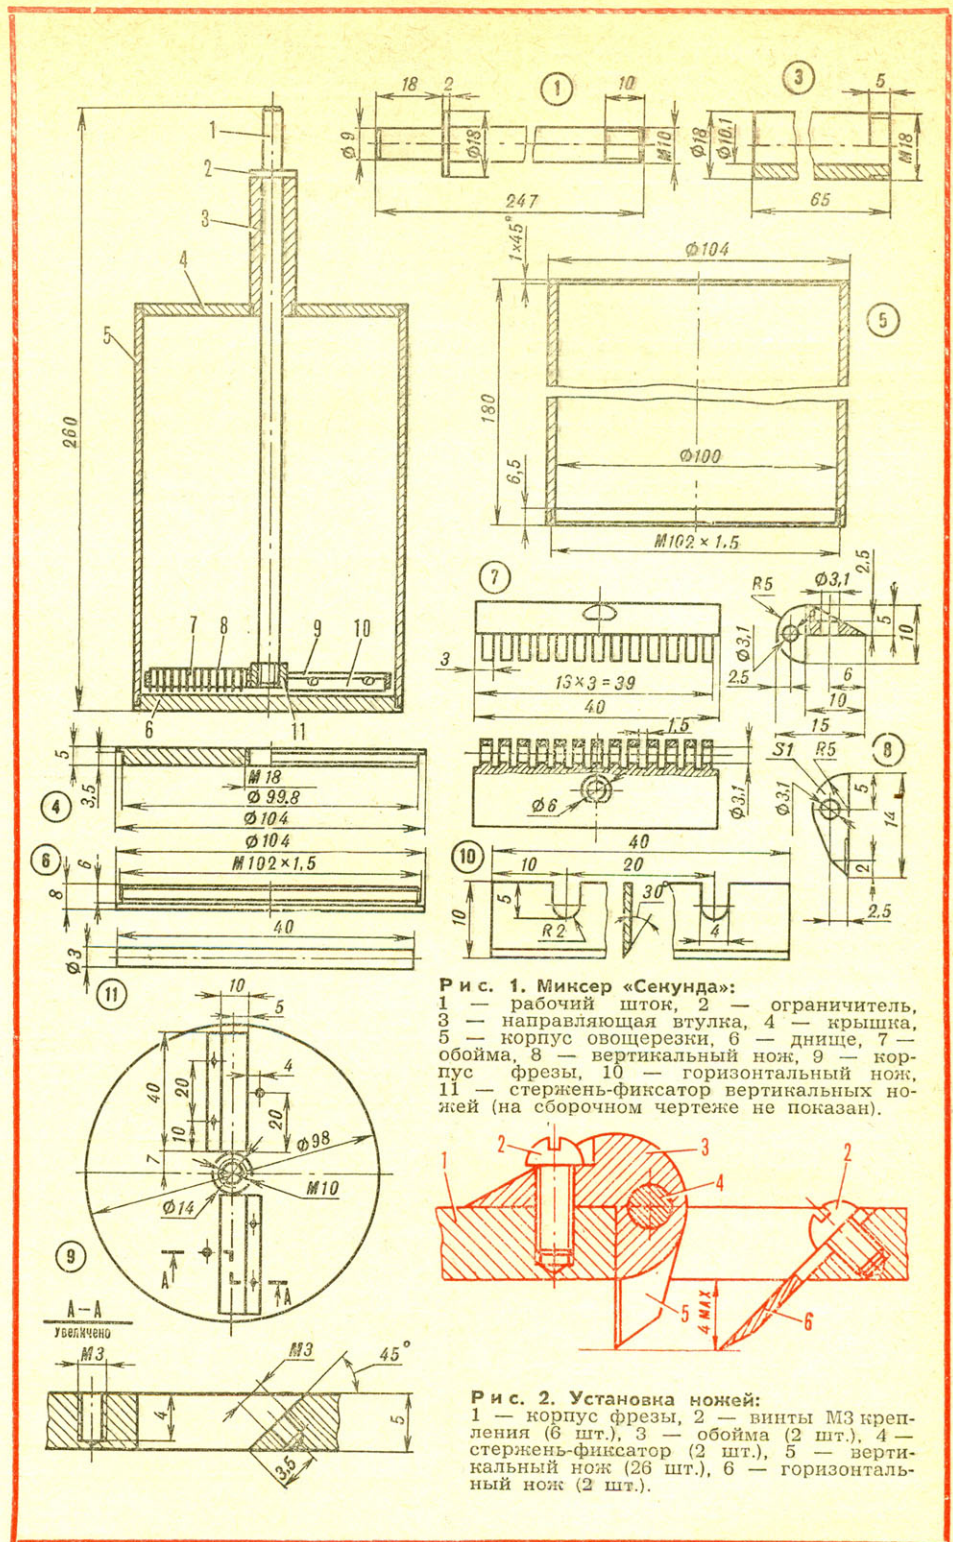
Миксер «Секунда»: 1 — рабочий шток, 2 — ограничитель, 3 — направляющая втулка, 4 — крышка, 5 — корпус овощерезки, 6 — дно, 7 — обойма, 8 — вертикальный нож, 9 — корпус фрезы, 10 — горизонтальный нож, 11 — стержень-фиксатор вертикальных ножей (на сборочном чертеже не показан).
